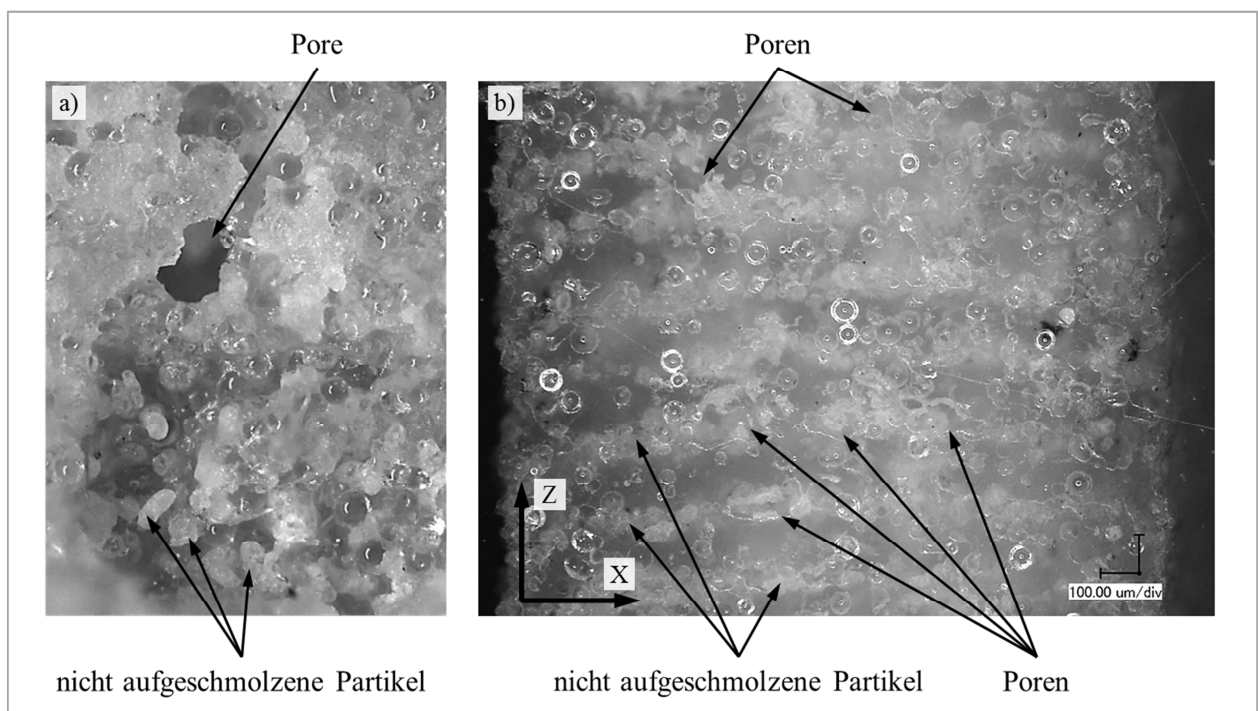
Bild a) Bruchfläche eines Probestabs mit deutlich ausgeprägter Pore und gut erkennbaren nicht aufgeschmolzenen Partikeln; Bild b) Schliffbild einer Z-Probe in Seitenansicht mit deutlich erkennbarem Schichtaufbau
